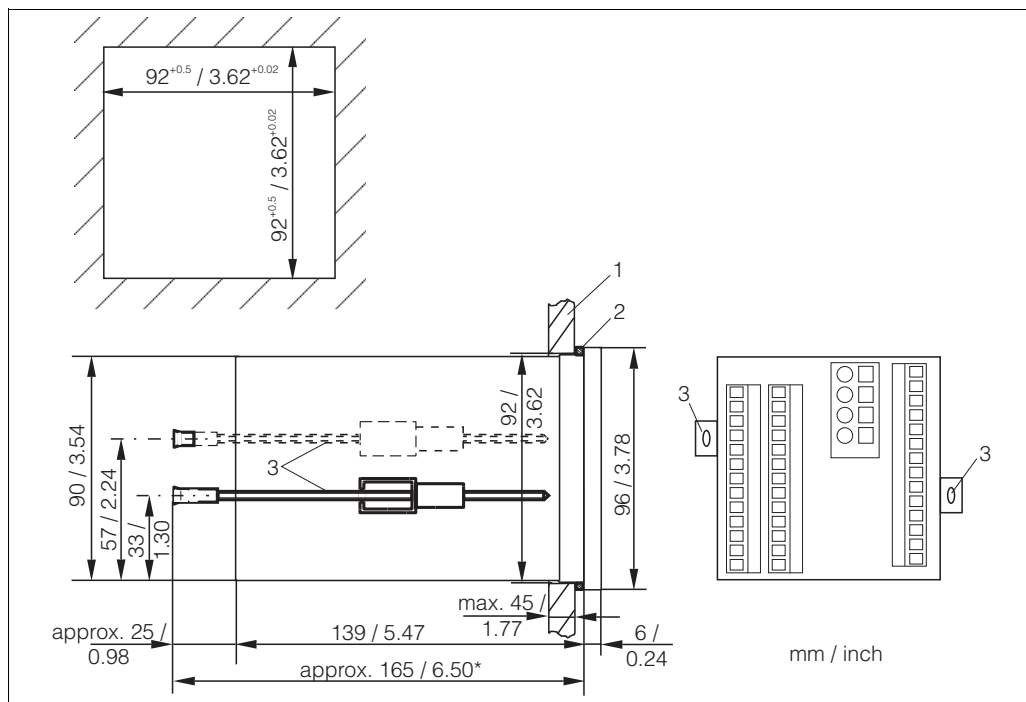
Fissaggio del trasmettitore per montaggio a fronte quadro
